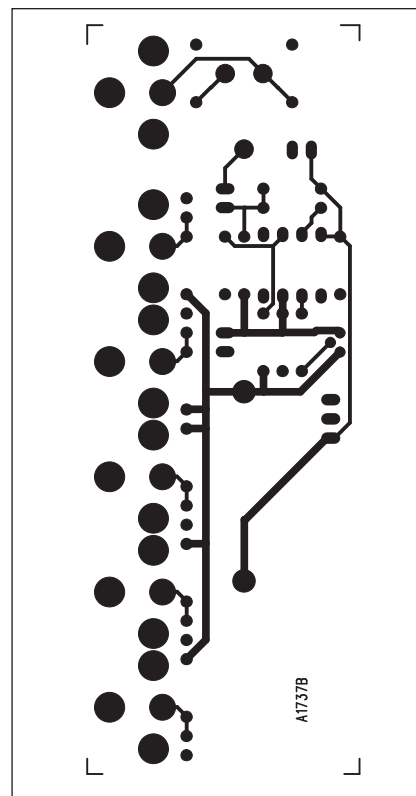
Obrazec desky spojů rozbočovače (strana TOP)
